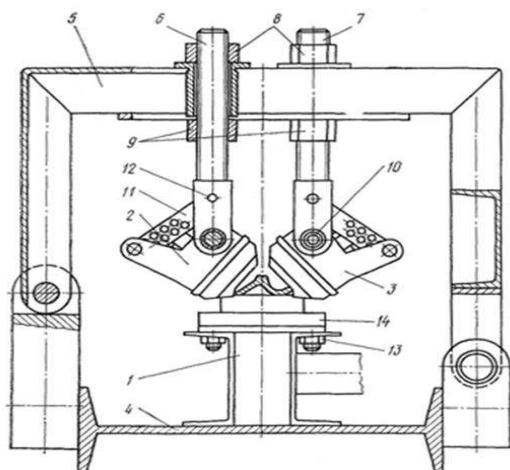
Универсальные устройства для ТП-ТМУ фасонных профилей конструкции УкрНИИМет: 1, 2, 3 – коллектора; 4 – несущая балка; 5 – ребро короба; 6, 7 – винт; 8, 13 – гайки; 9 – фиксаторы винтов; 10 – оси; 11 – планки; 12 – фиксаторы планок; 14 – стол
